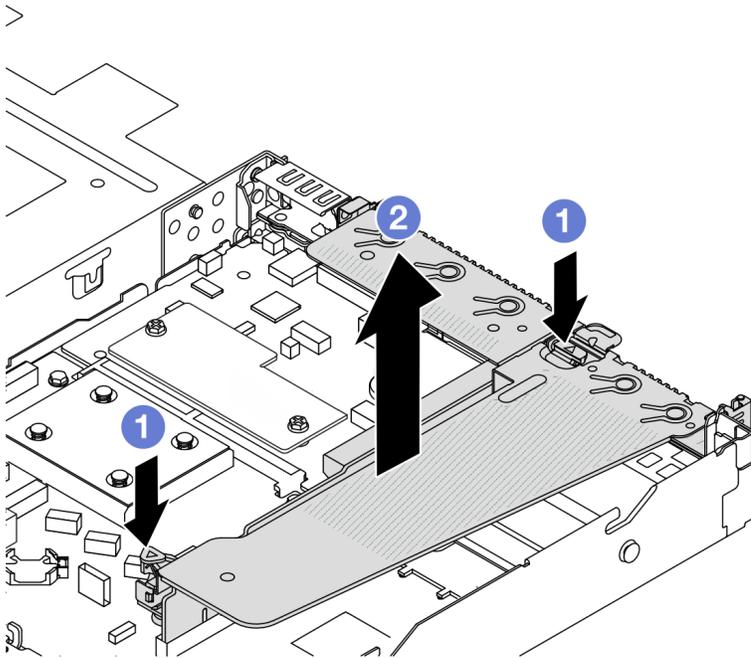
Entfernen einer hinteren Adapterhalterung
